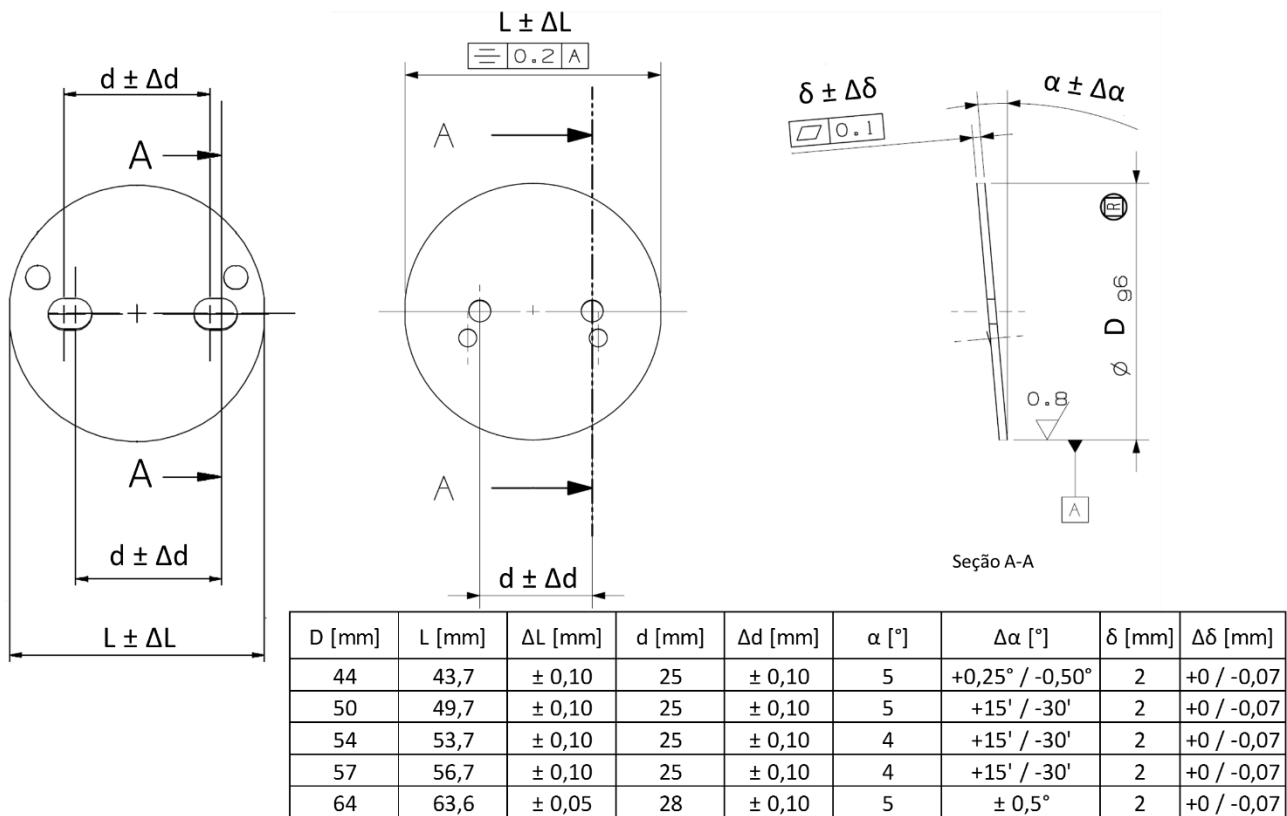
Exemplos de dimensões básicas da válvula de aceleração.
